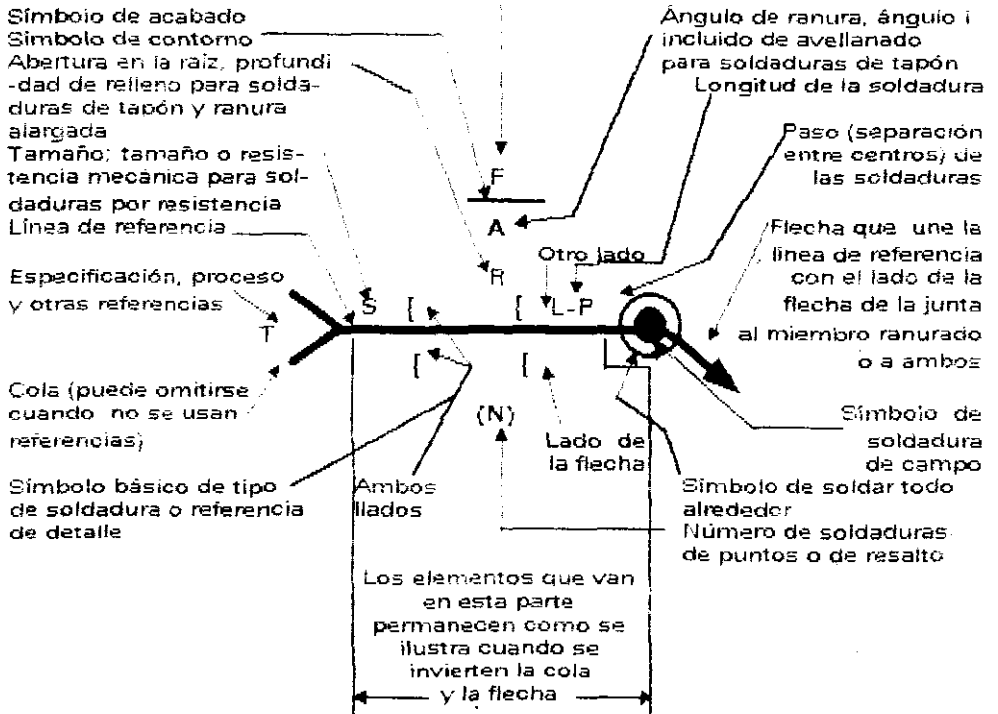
SÍMBOLO COMPLETO DE SOLDADURA
